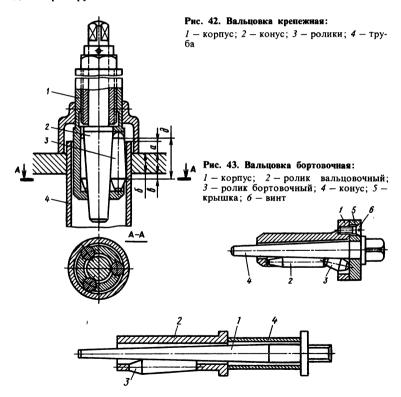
Вальцовка для трубок: I — конус; 2 — корпус; 3 — ролик; 4 — ограничительная втулка
